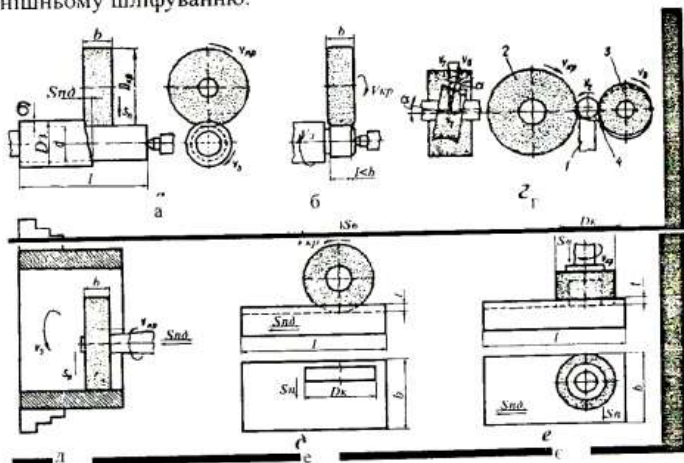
Схеми шліфування: 1 – заготовка, 2 – шліфувальний круг, 3 – оправка, 4 – ведучий круг, 5 – ніж, 6 – стіл верстата
